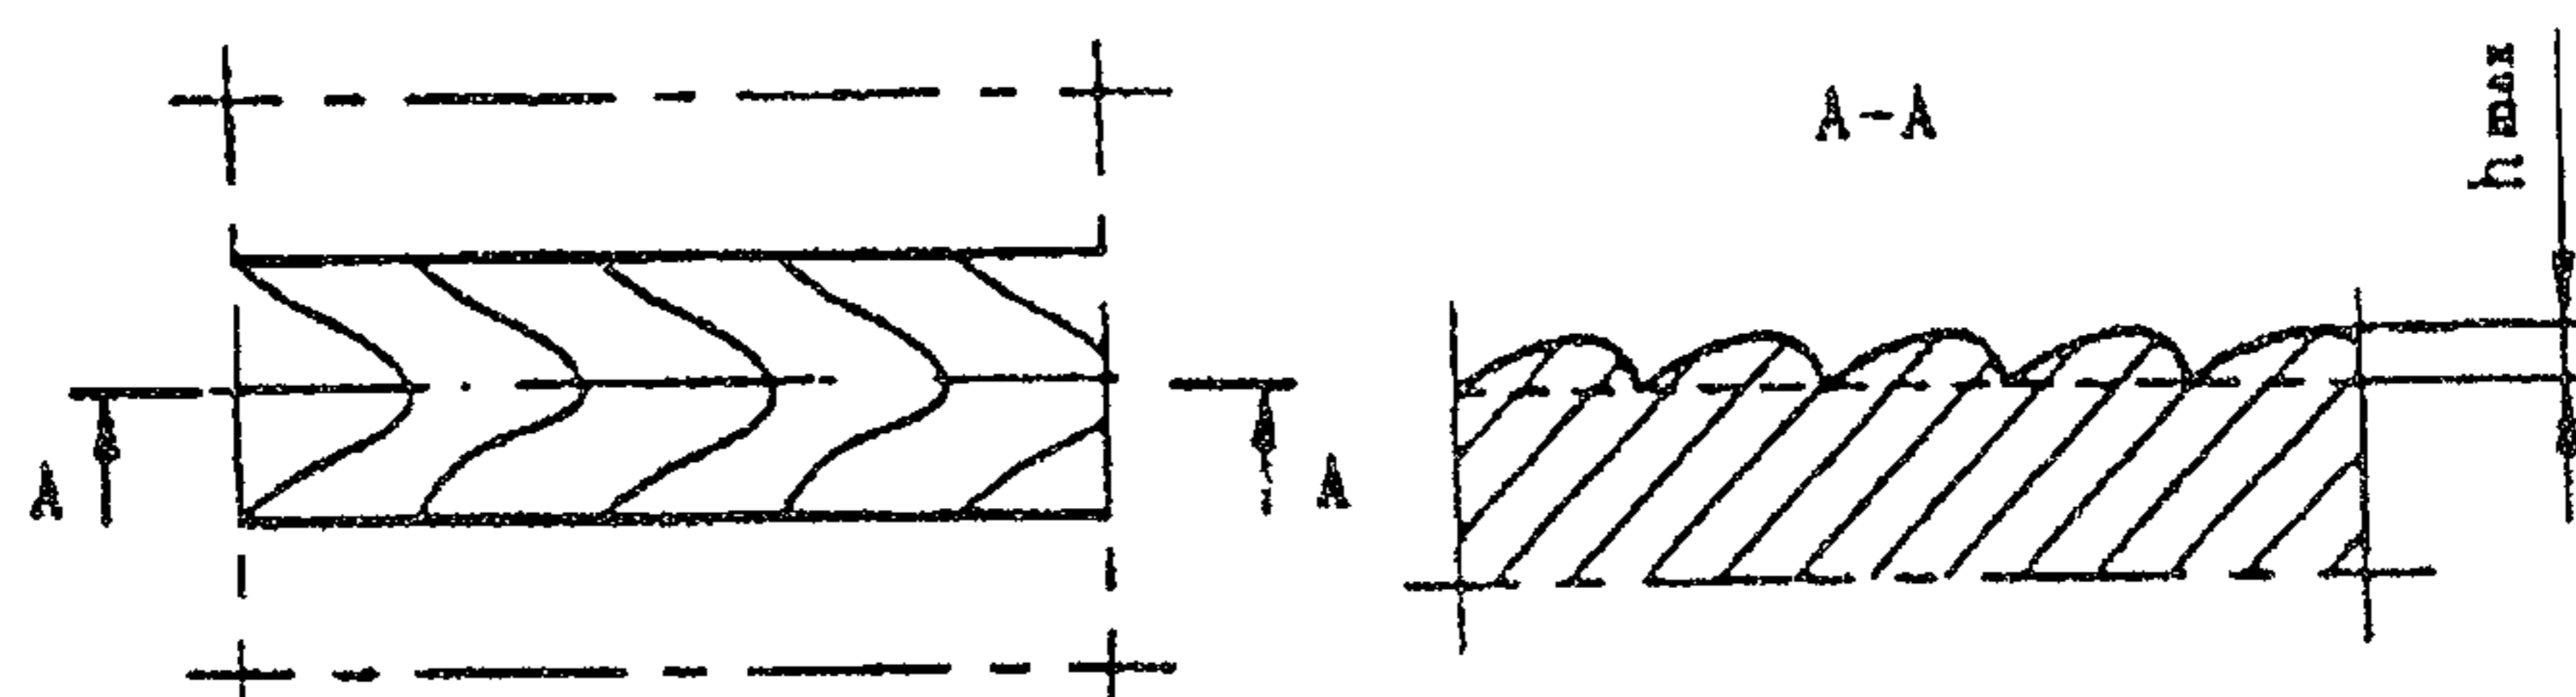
Чешуйчатость сварного шва
